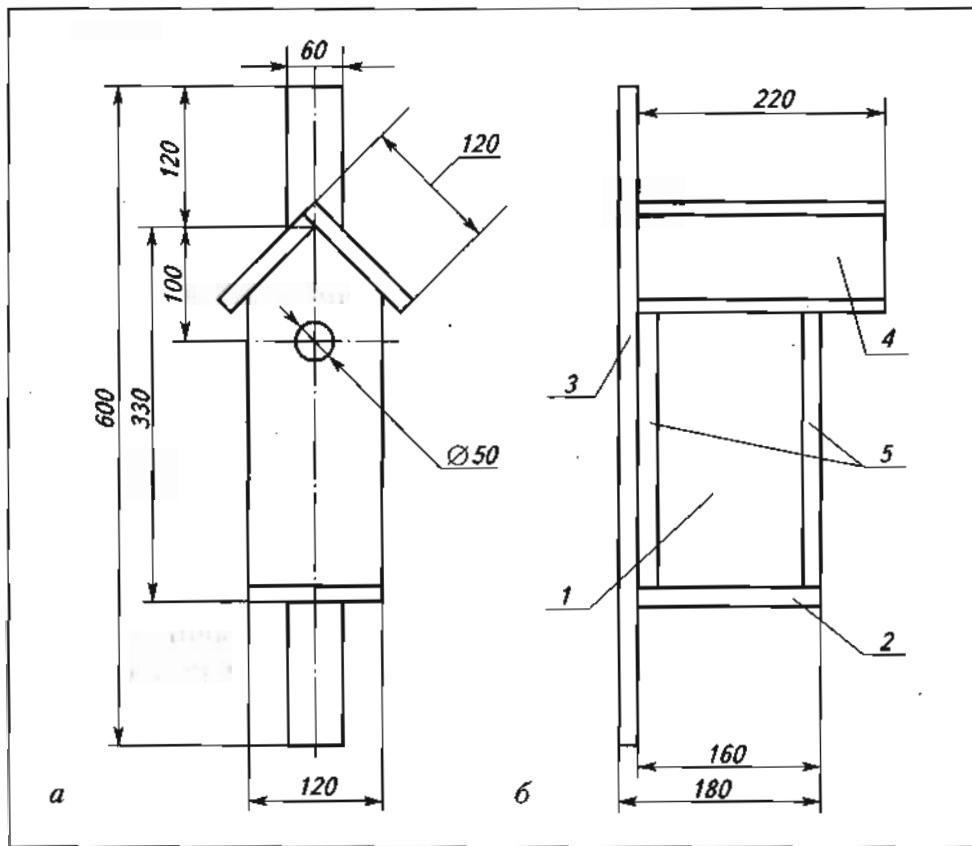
Чертёж домика для птиц: а – главный вид, б – вид слева:
